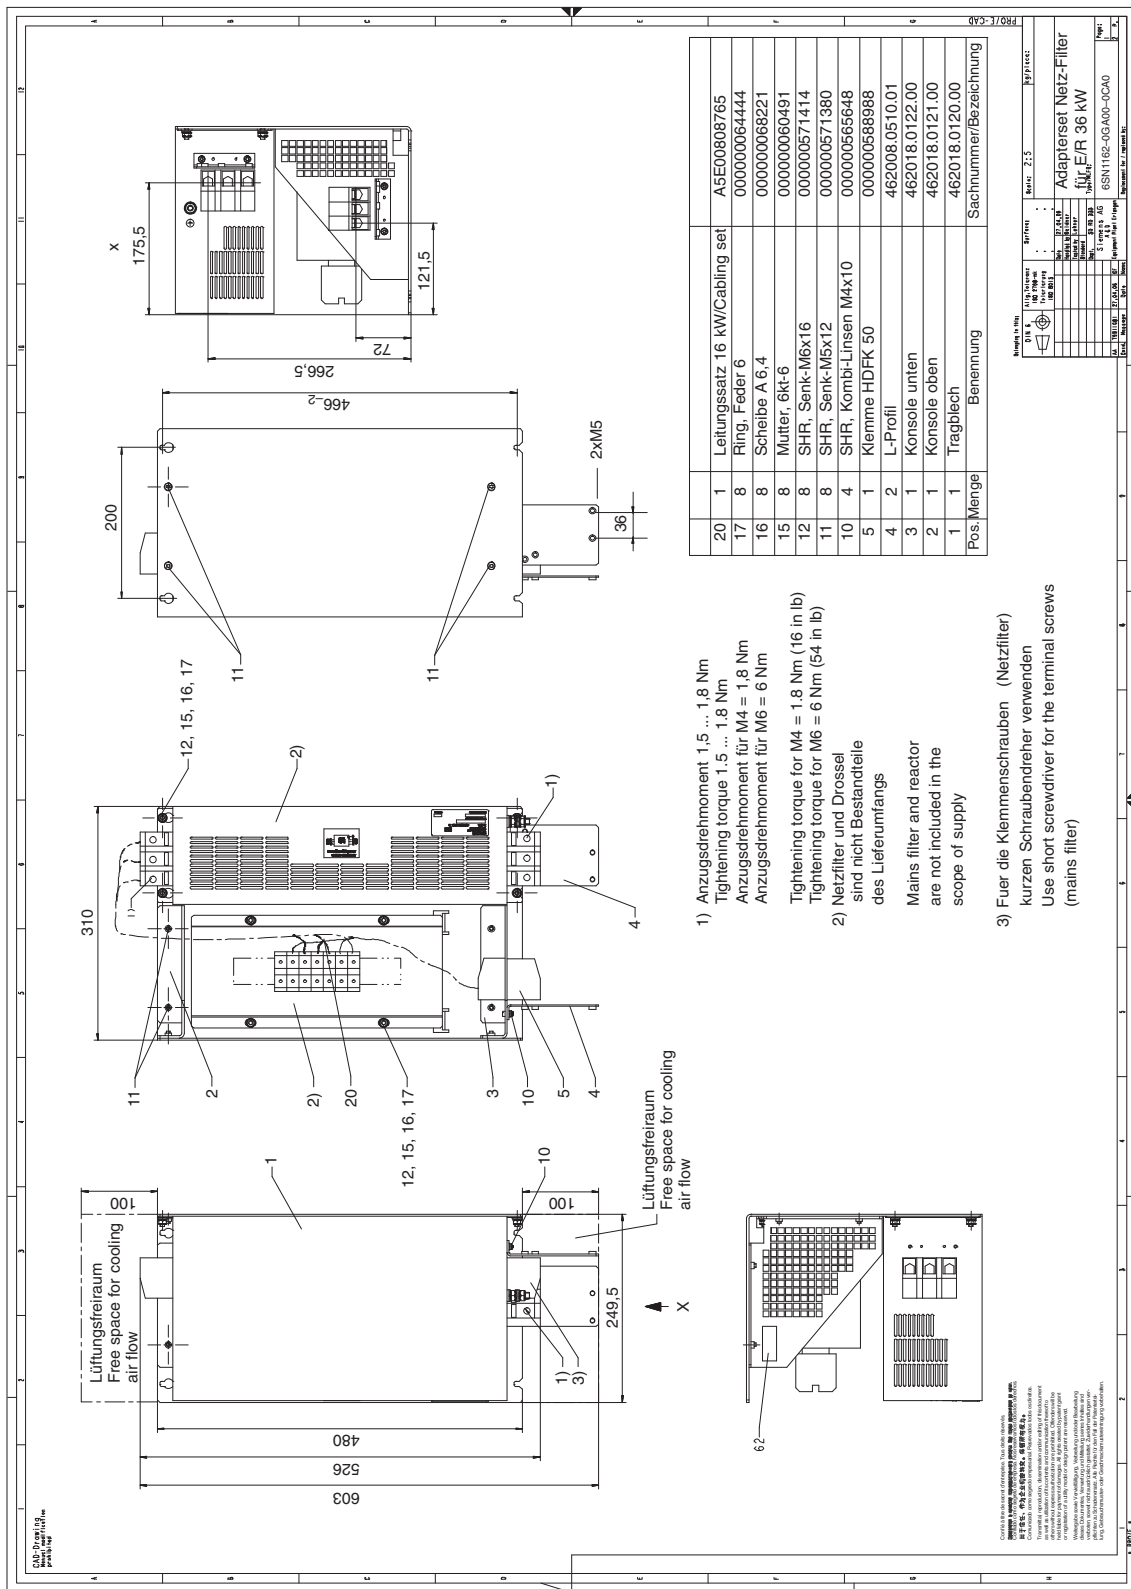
Adapterset Netzfilter für E/R-Modul 36 kW, 6SN1162-0GA00-0CAx; Maßblatt
